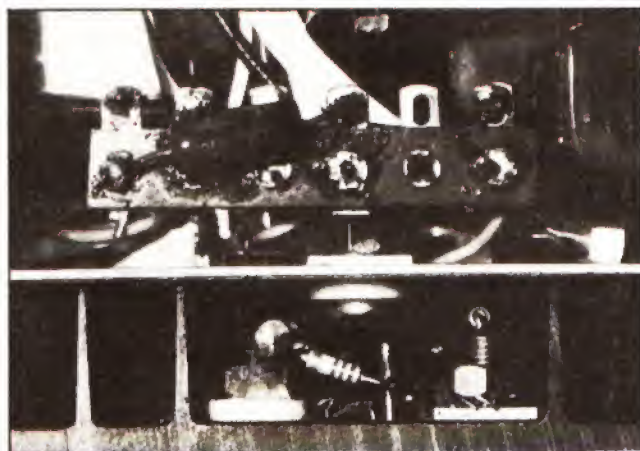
Un ensemble de deux cosses à souder, à trous de 3 mm, une ayant été coupée assez court, soudée sur l'autre que l'on a pliée, constitue une « équerre » simplifiée pour la fixation du circuit imprimé.
